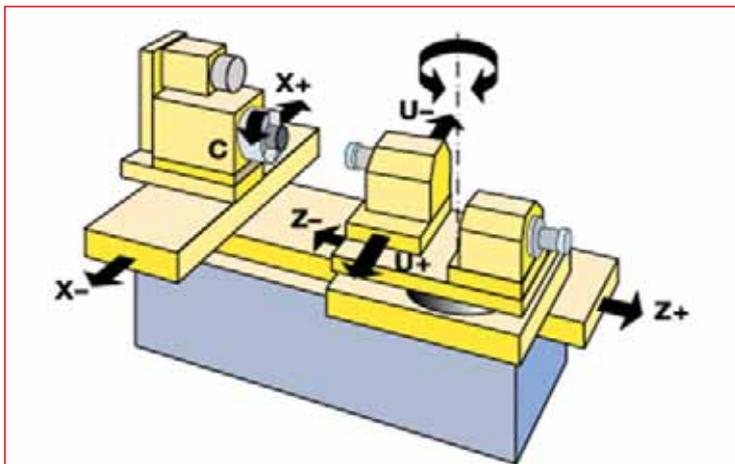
Компонка профишлифовальных станков мод. 110 CNC CG и 150 CNC CG
